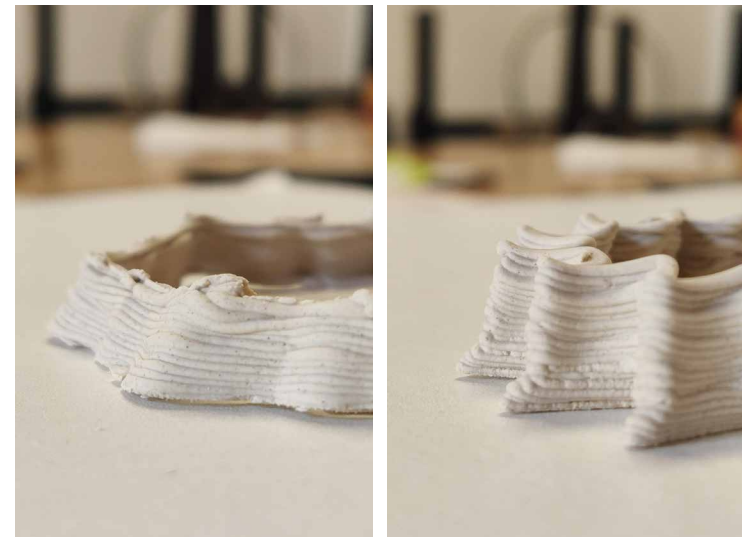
Fotos de pruebas de impresión realizadas con distintos tamaños de boquilla, A la izquierda boquilla de 1.3 7mm a la derecha boquilla de 1.65mm.
